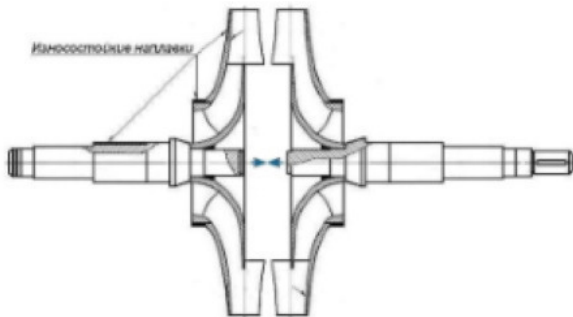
Схема сборки половинок цельносварного ротора центробежного насоса двустороннего входа
